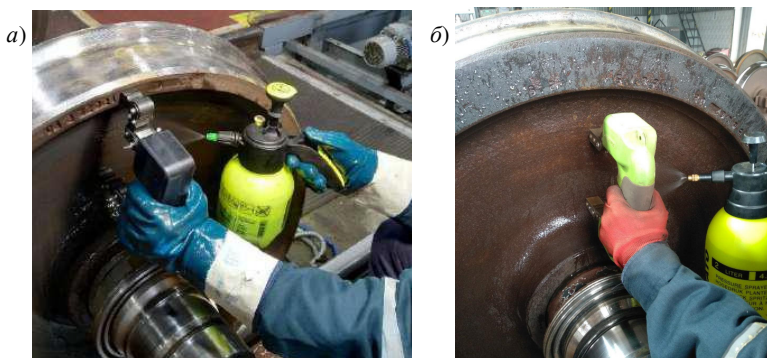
Магнитопорошковый контроль цельнокатаного колеса («ручной» способ):
